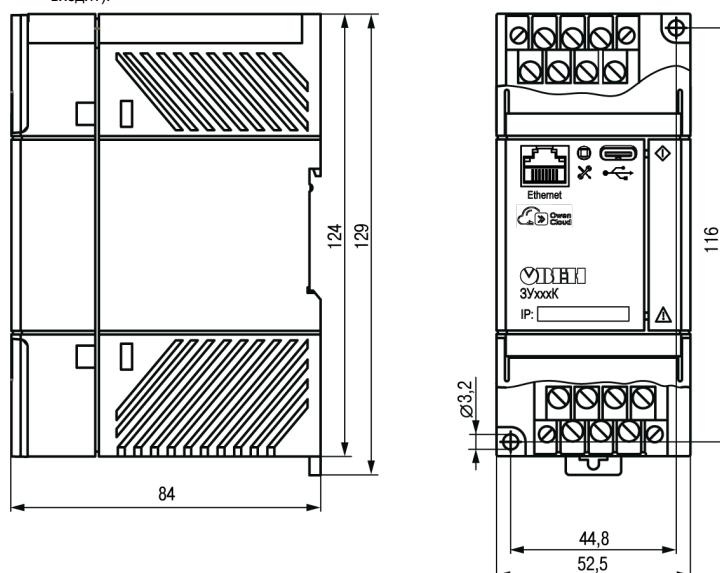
Внешний вид, габаритные и установочные размеры прибора
